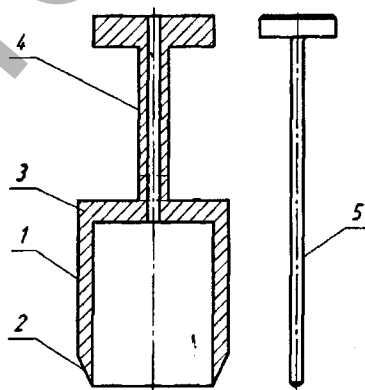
Устройство для изготовления цилиндрических obturators:
